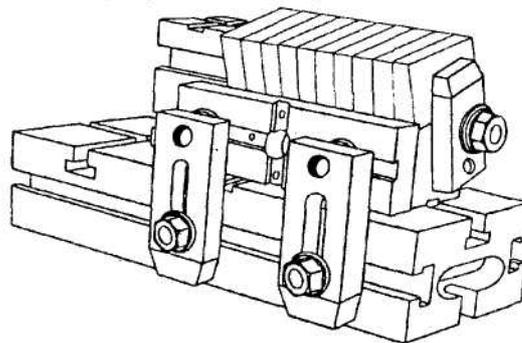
Багатомісне пристосування для фрезерування заготовки
